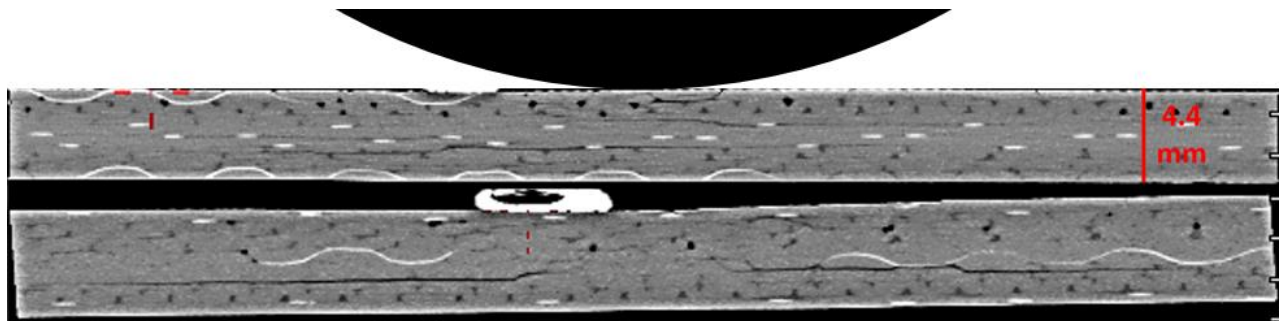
Vue de côté d'une éprouvette vieillie en eau de mer impactée à 30J
